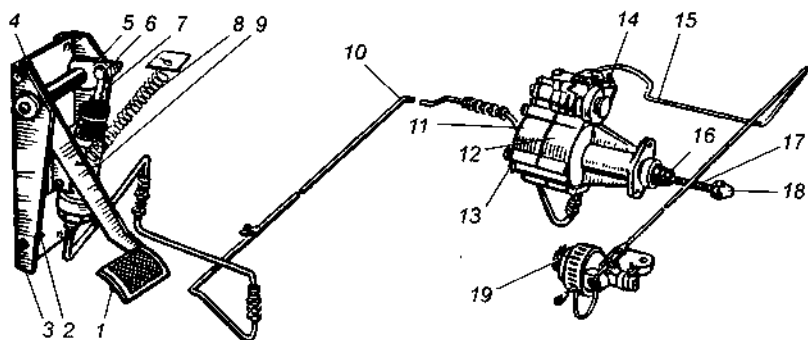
Механизм привода выключения сцепления автомобиля марки «КамАЗ»: *1* — педаль; *2, 4* — нижний и верхний упоры соответственно; *3* — кронштейн; *5* — рычаг; *6* — эксцентриковый палец; *7* — толкатель поршня; *8* — оттяжная пружина; *9* — главный цилиндр; *10* — гидравлический трубопровод; *11, 12* — передний и задний корпуса пневмоусилителя соответственно; *13* — пробка; *14* — перепускной клапан; *15* — пневматический трубопровод; *16* — защитный чехол; *17* — толкатель поршня пневмоусилителя; *18* — сферическая регулировочная гайка; *19* — редукционный клапан делителя передач
